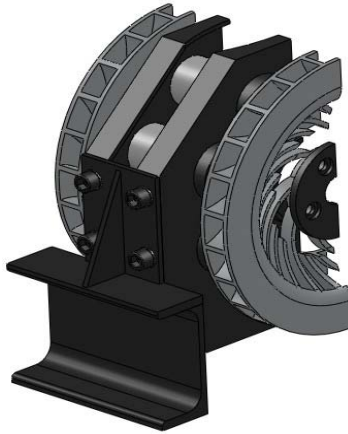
Montaje del freno sobre chapa soldada en L.
